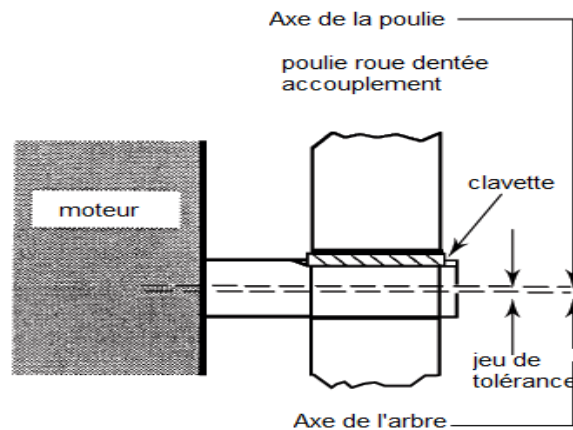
Défauts de tolérances de fabrication et d'assemblage
